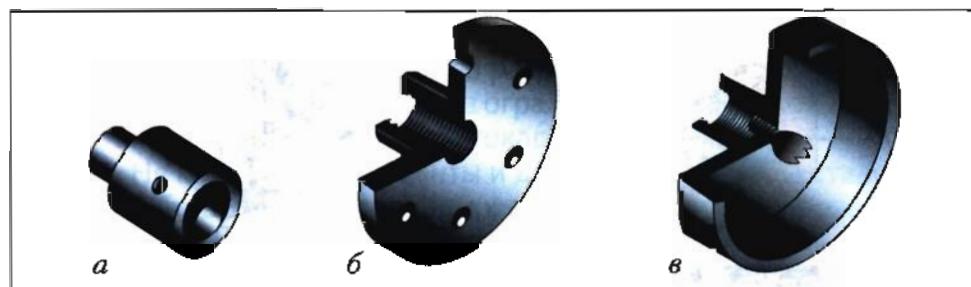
Шпиндельные приспособления для крепления заготовок при точении: *а* – патрон, *б* – планшайба, *в* – трезубец
